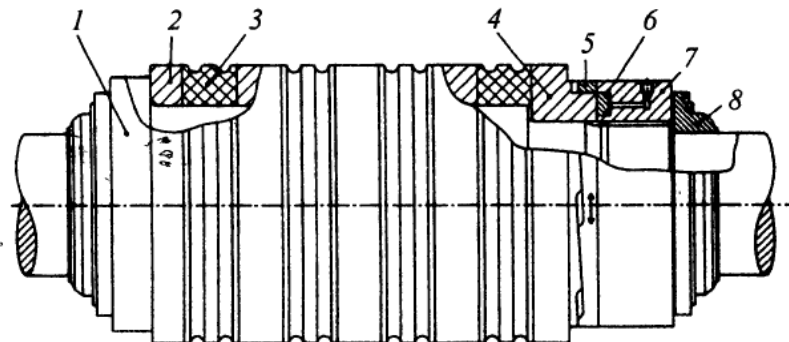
Валок «Кафікс» фірми "Kark Maschinenfabric GmbH"
